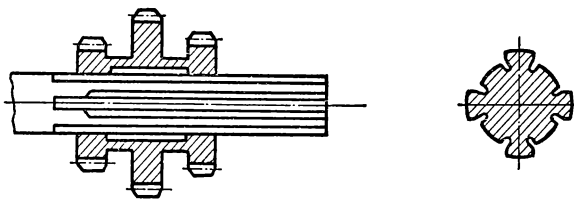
Четырехшлицевый вал с блоком зубчатых колес
